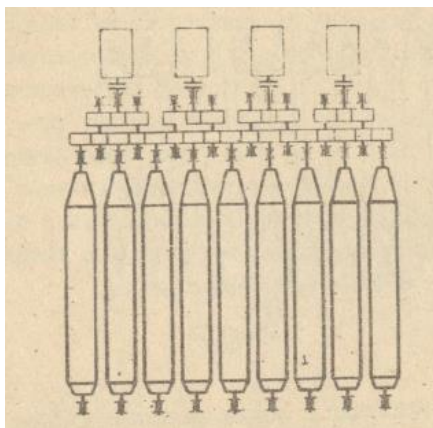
Привод роликов рольганга через двухрядный цилиндрический редуктор
